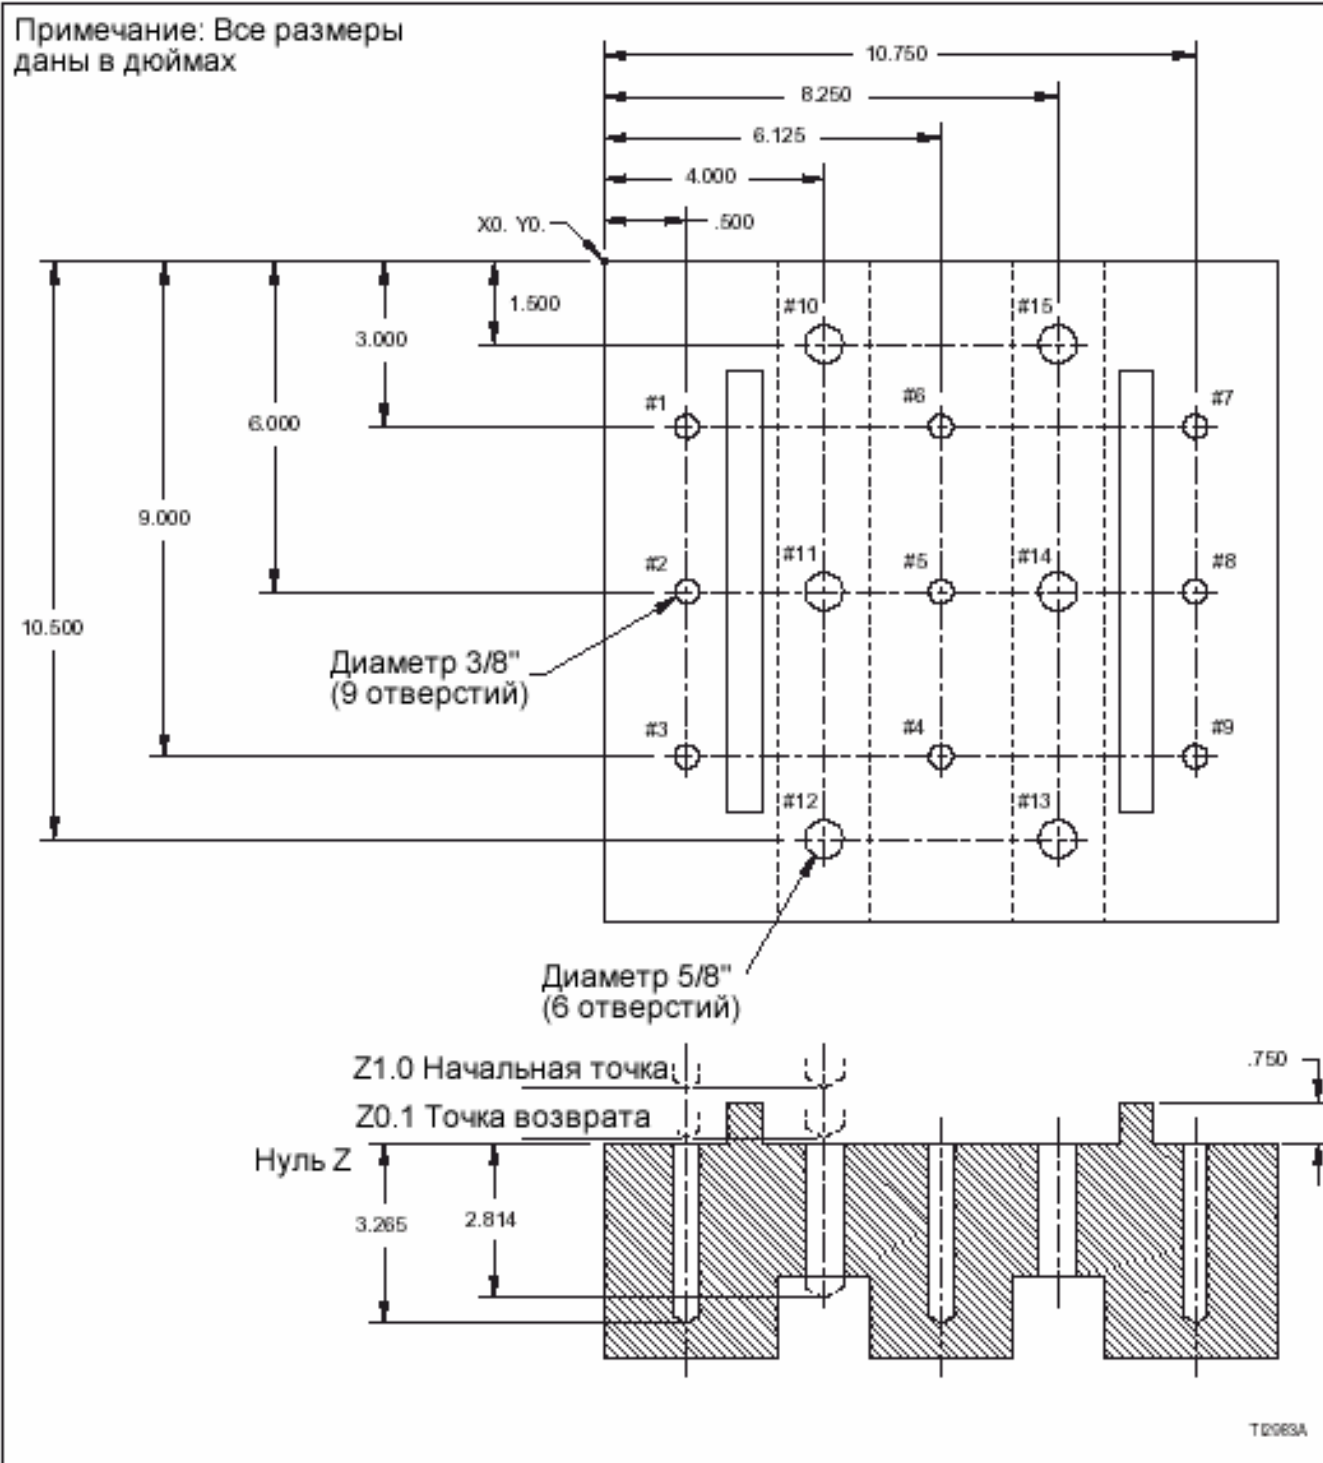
Типовая заготовка: Сверление нескольких отверстий.
